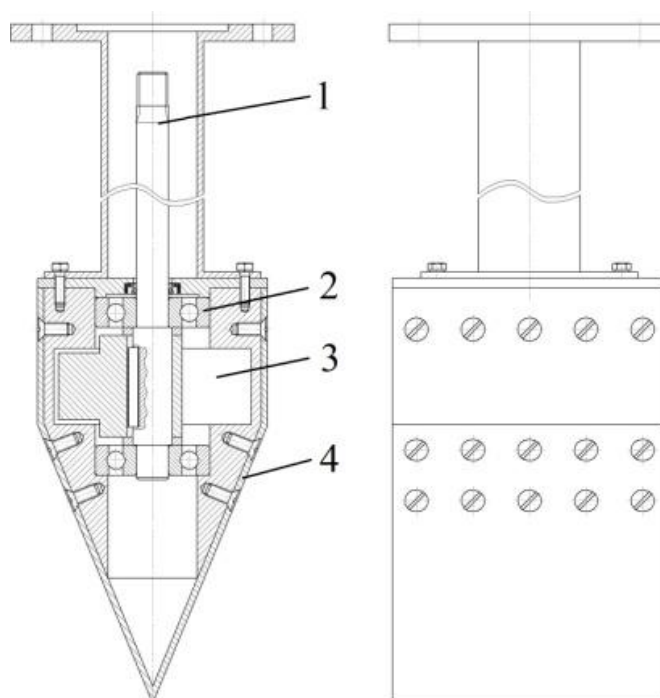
Клиновое подбойник: 1 – вал; 2 – подшипник; 3 – дебаланс; 4 – корпус
